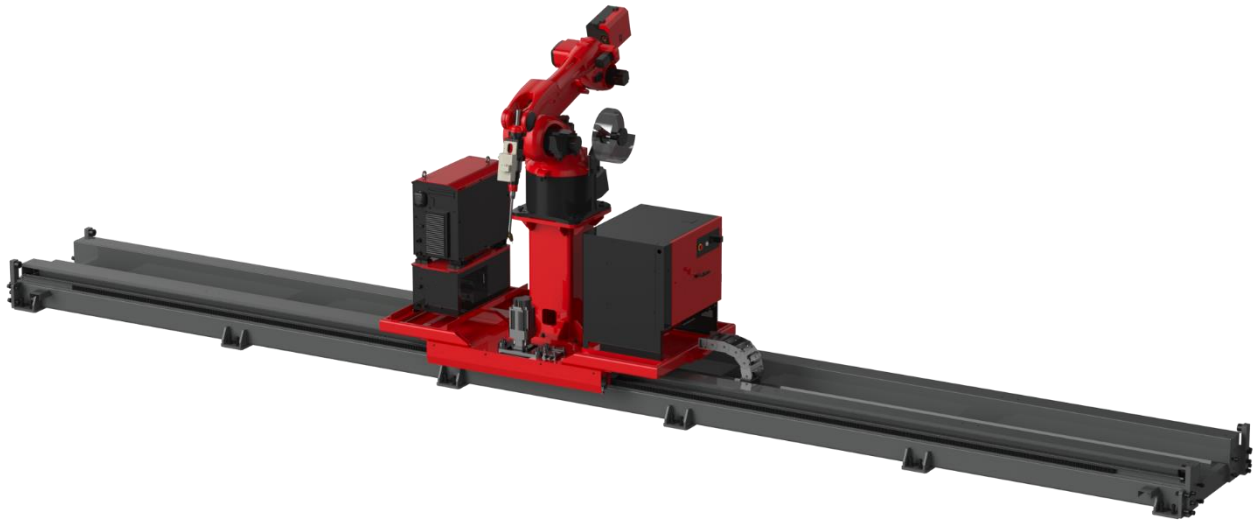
Семиосьова наземна робоча станція зварювального робота
